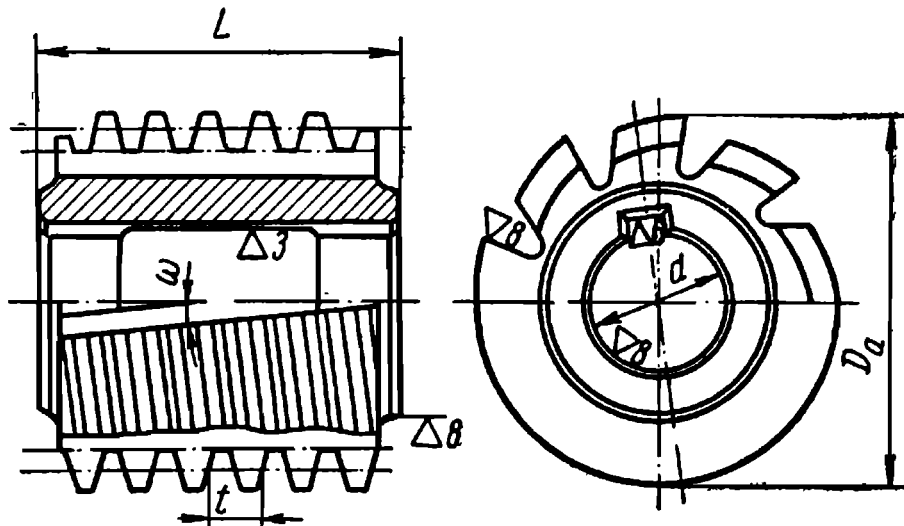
Червячная фреза для нарезания цилиндрических колес
